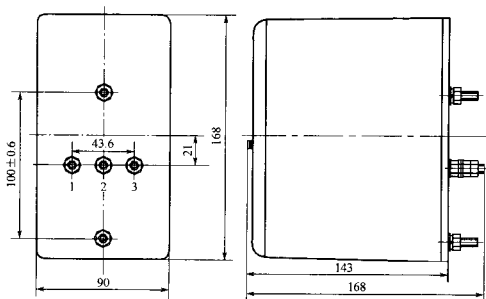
HF-25 型防护盒的安装尺寸与外形参考尺寸
